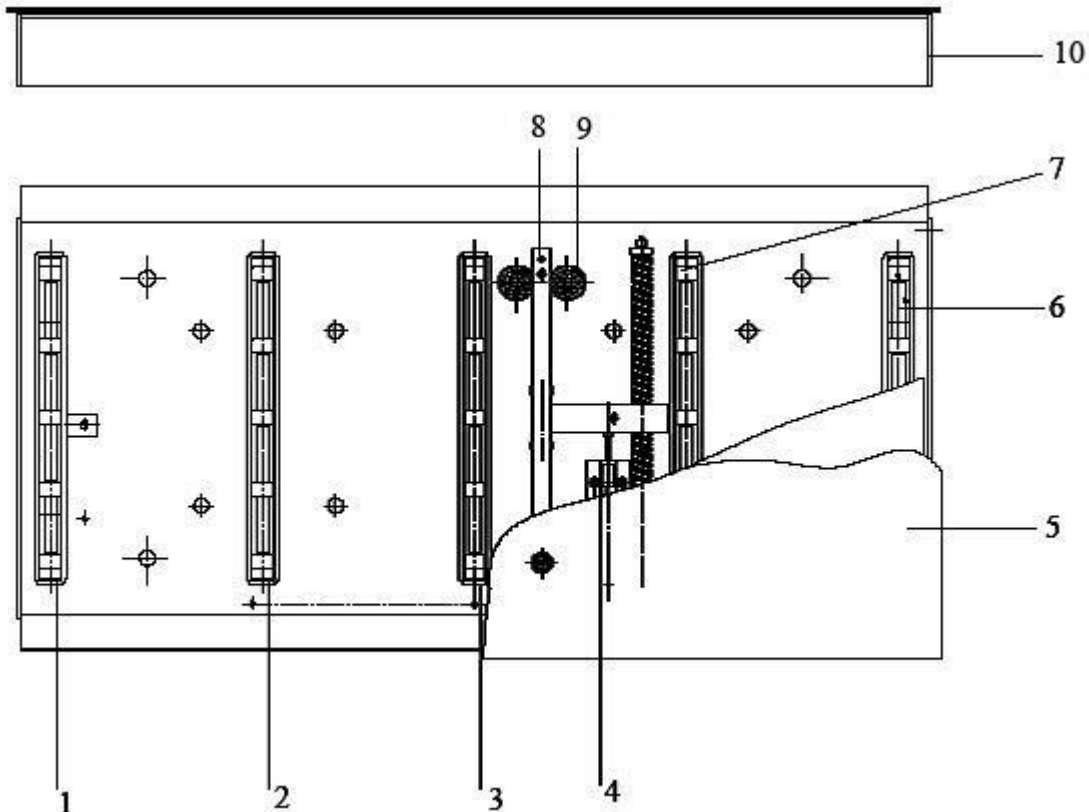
Конструкція стенда для експрес-діагностики положення коліс: 1,2,3,6,7 – полозок; 4 – вимірювальний датчик; 5 – вимірювальна плита; 8 – пристрій зрушення; 9 – напрямні; 10 – короб.
